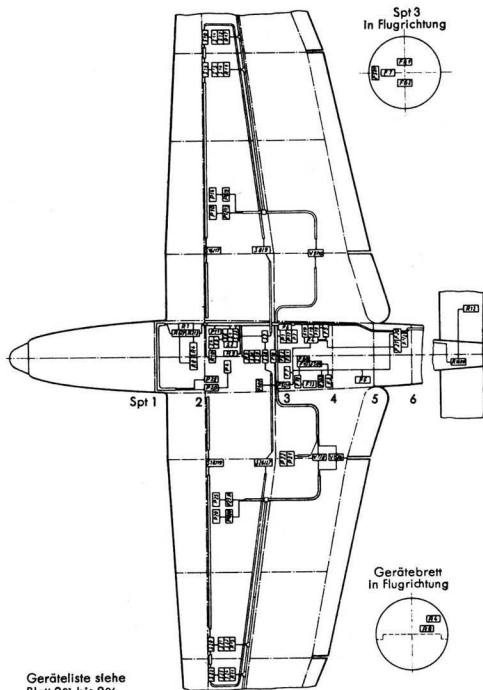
Lageplan der Bordfunk- und Bewaffnungsanlage (8700—7129)
